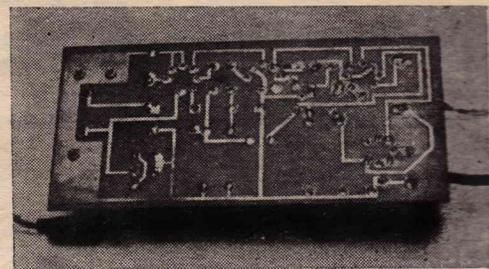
Le dessous du panneau. On voit le circuit imprimé et toutes les connexions soudées.
